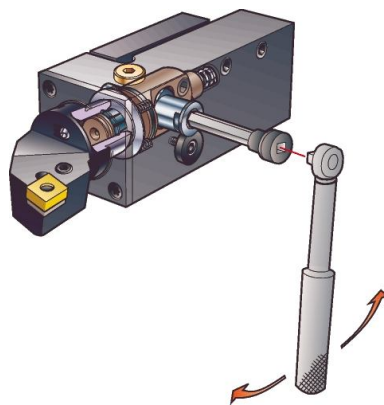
Механизм с лепестковой цангой с сегментами для закрепления инструмента в револьверной головке.
